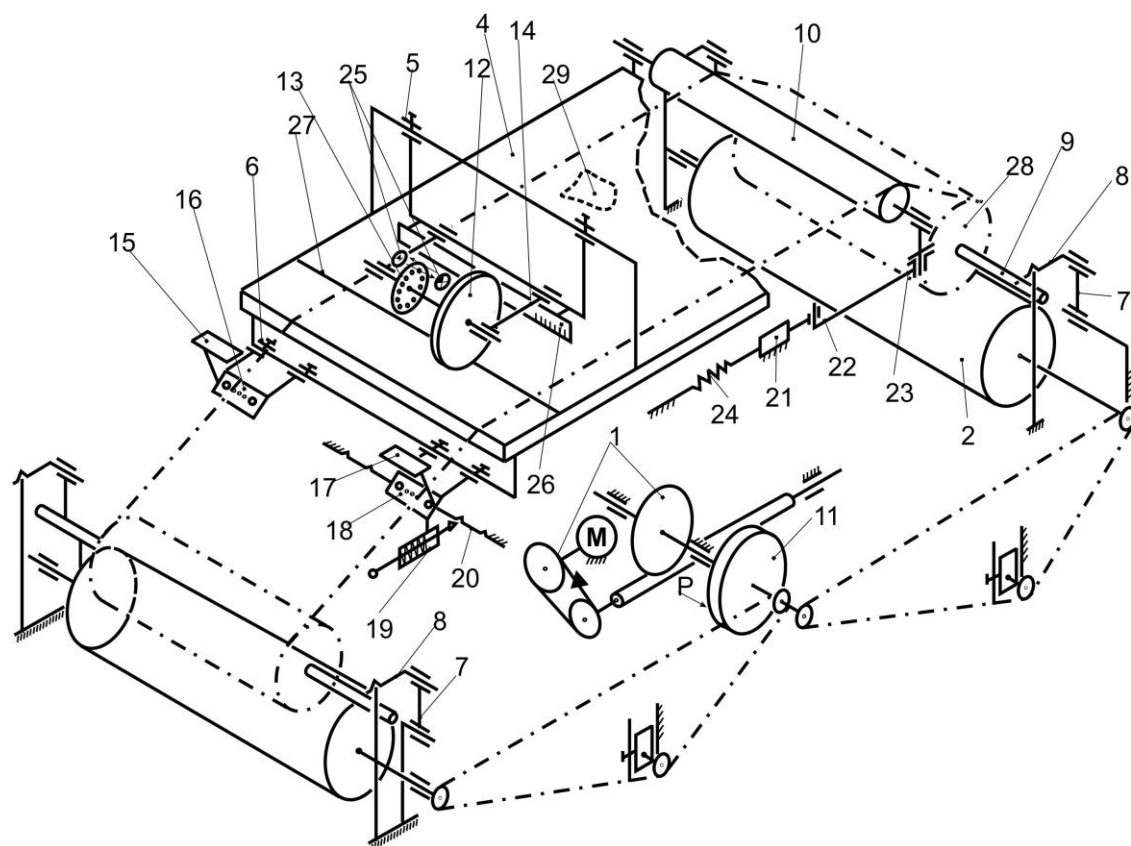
Кинематическая схема станка для промера и разбраковки швейных материалов
